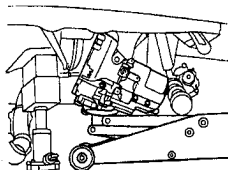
Установка троплейного домкрата под коробкой передач при ее снятии [См. Раздел 4]
